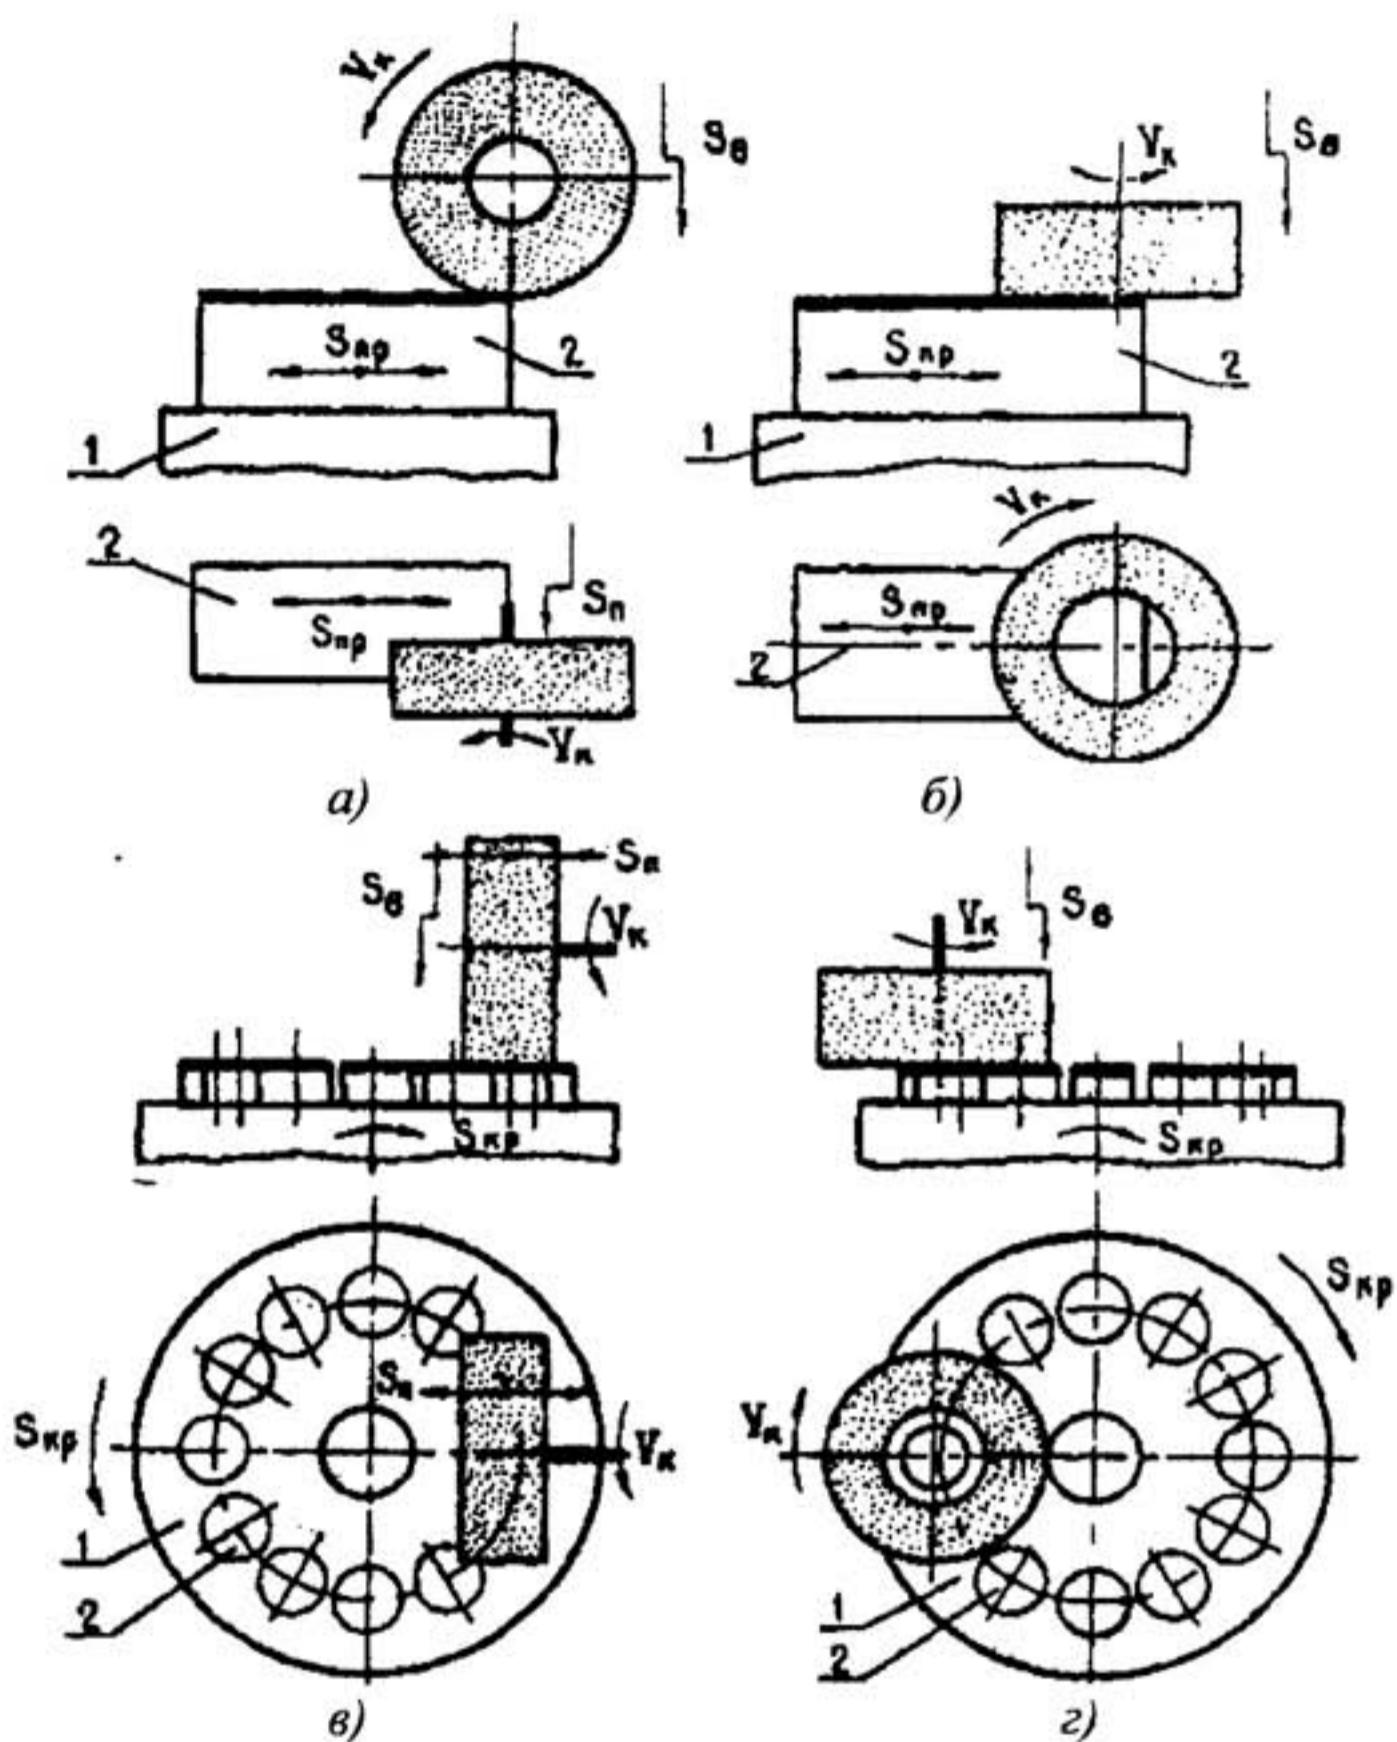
Схемы обработки заготовок на плоскошлифовальных станках
